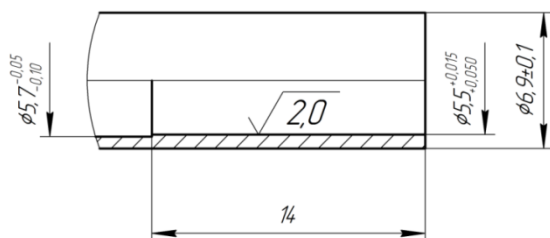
Пассивные рабочие инструменты для размерной обработки отверстий диаметром от 3 до 15 мм
